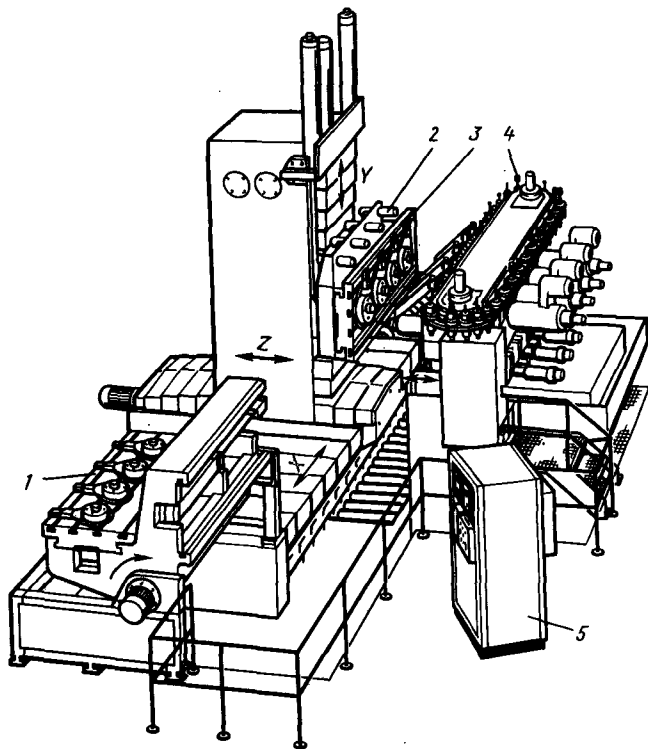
Станок для многошпиндельной обработки (специальный многоцелевой станок с перемещениями по оси X — 1200 мм, по оси Y — 1200 мм и по оси Z — 800 мм): 1 — накопитель заготовок; 2 — устройство для проверки установки инструмента; 3 — многоспунный спутник; 4 — инструментальный магазин; 5 — система ЧПУ
